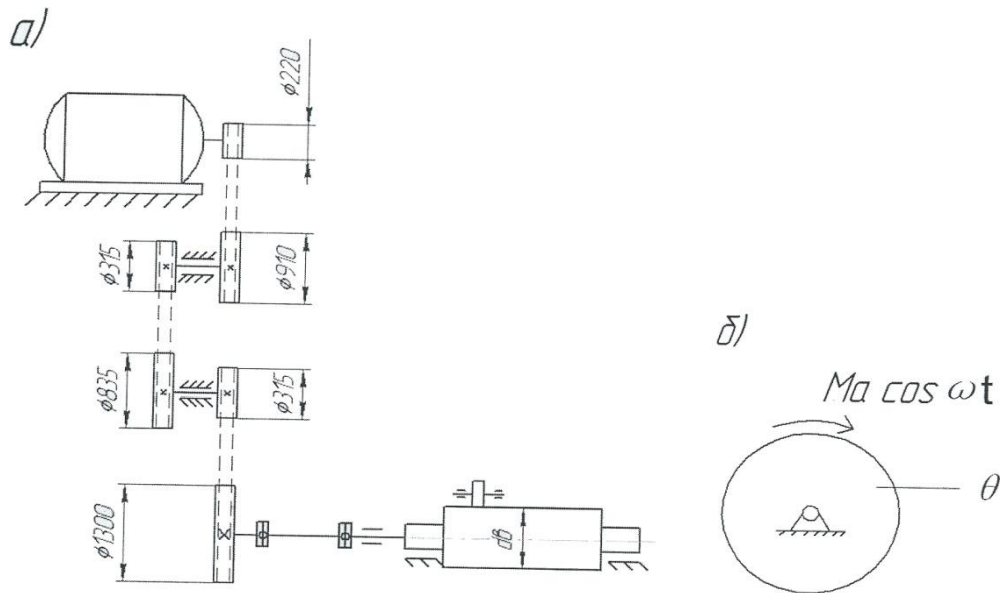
Схема привода шлифуемого вала (а) и модель крутильно-вращательных колебаний вала (б)
